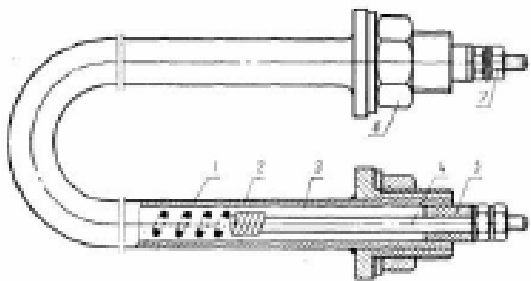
Устройство ТЭНа. Трубчатый электронагреватель (ТЭН) герметического исполнения: 1 — нихромовая спираль; 2 — трубка; 3 — наполнитель; 4 — выводная шпилька; 5 — герметизирующая втулка; 6 — гайка для крепления; 7 — выводы.
